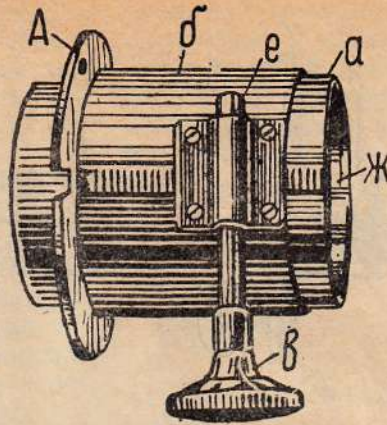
Кремальера. А — фланец для крепления кремальеры к головке проектора; а — внутренняя труба; б — внешняя труба; в — ось с барашком; е — накладка; ж — зубчатая рейка.
